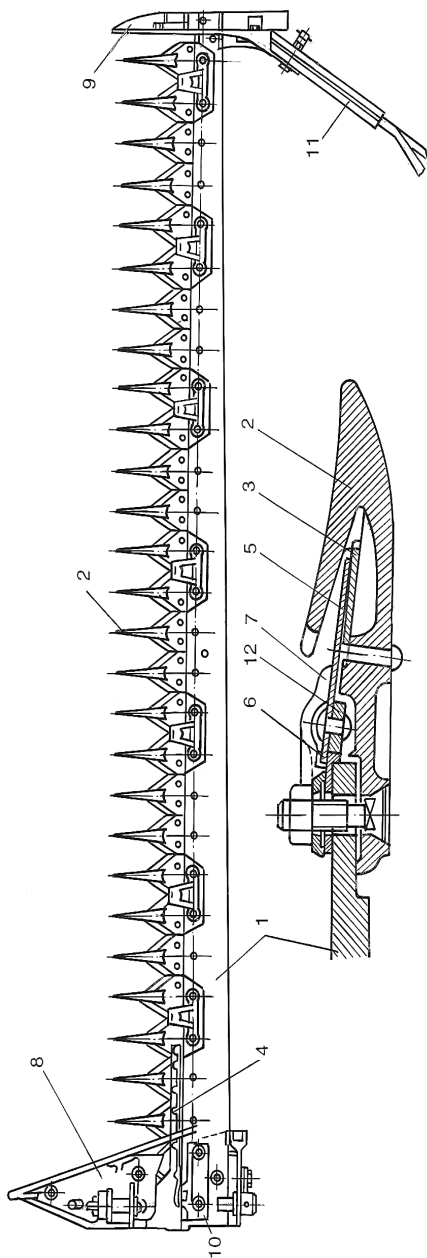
Сегментно-пальцевый режущий аппарат: 1 – пальцевый брус; 2 – палец; 3 – вкладыш пальца; 4 – головка ножа; 5 – сегмент ножа; 6 – пластина трения; 7 – прижим ножа; 8 – внутренняя башмак; 9 – наружный башмак; 10 – направляющая головка ножа; 11 – левая доска; 12 – спинка ножа
